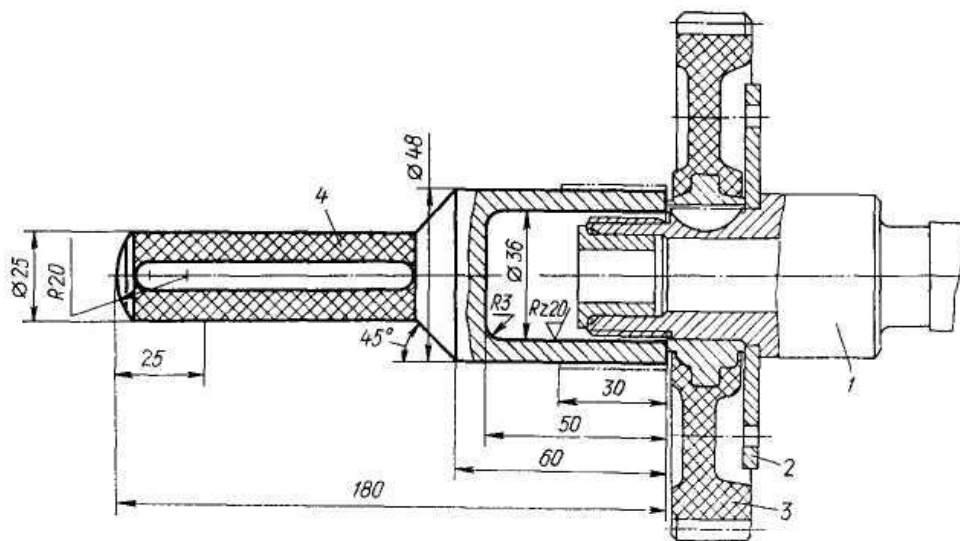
Оправка для напрессовки шестерни распределительного вала:
